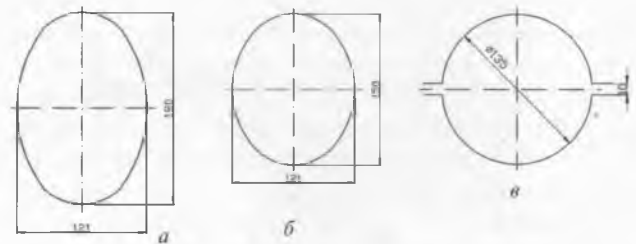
Вид заготовки (а, б) и инструмента (в) для моделирования прокатки овальной заготовки в круглом калибре
